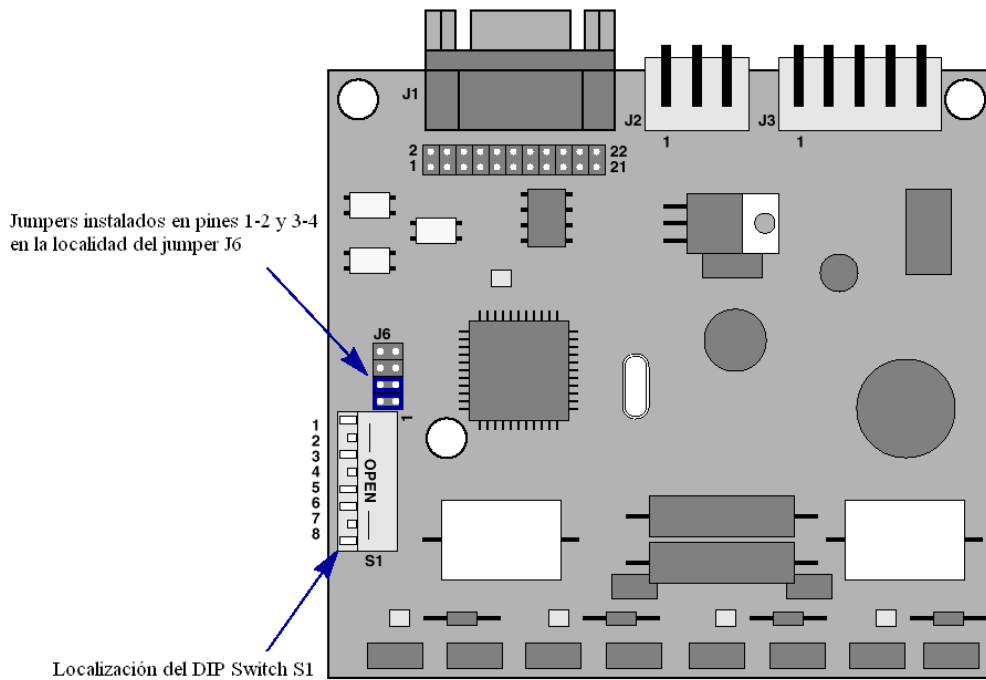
Localización del DIP switch de ocho posiciones (Fuente: Rotary fuel valve and position controller for gas turbines)
